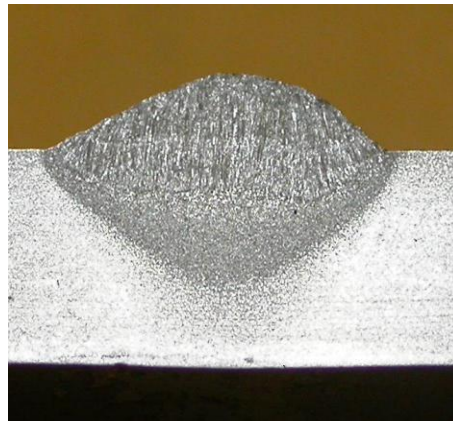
Muestra 1 usando soldadura FCAW con CO₂ como gas de protección
